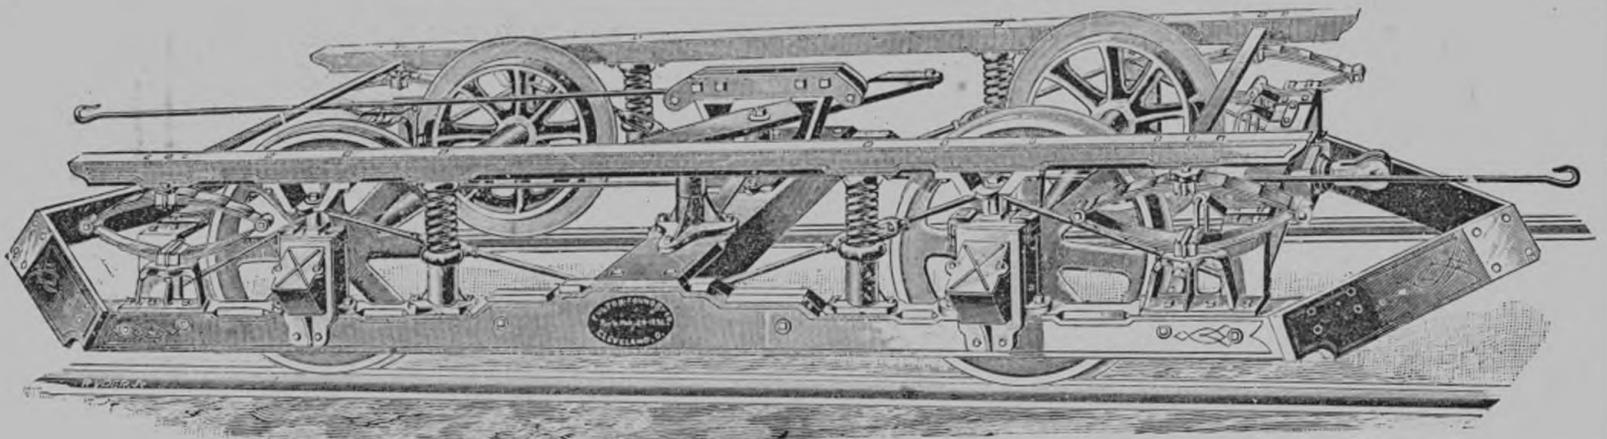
CHASSIS FULTON POUR TRACTION A CABLE
